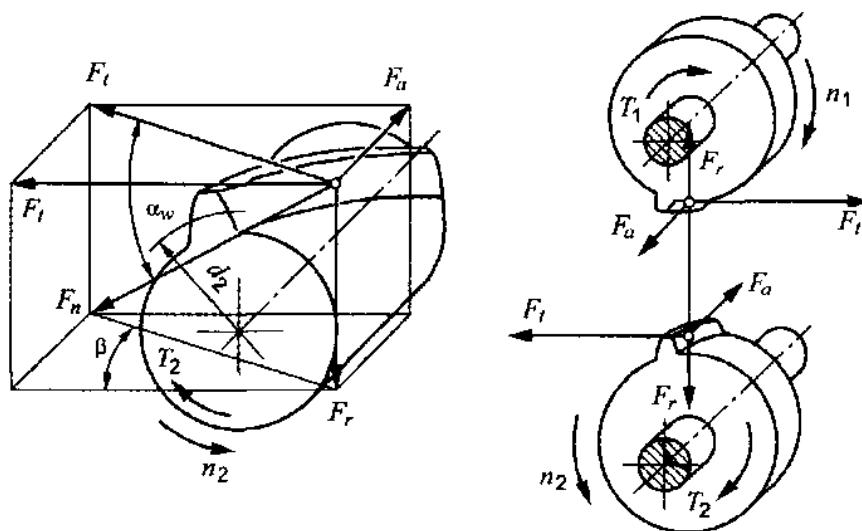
, б – Схема сил, действующих в косозубой цилиндрической передаче с разъединенными звеньями
